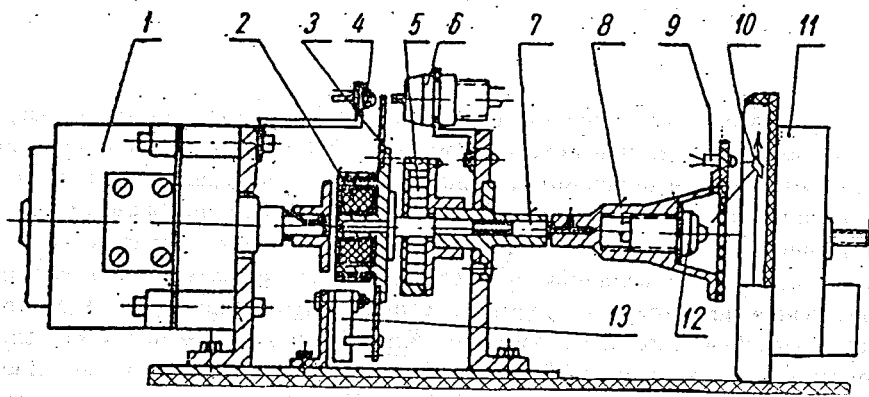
Конструкция электромеханического считывающего устройства. (1 — электродвигатель; 2 — электромагнитная муфта; 3 — диск-дискритизатор; 4, 9 — фотодиоды; 5 — возвратная пружина; 6, 12 — осветители; 7 — ось возвратной пружины; 8 — съемная головка; 10 — зеркало; 11 — стрелочный прибор; 13 — упор)
